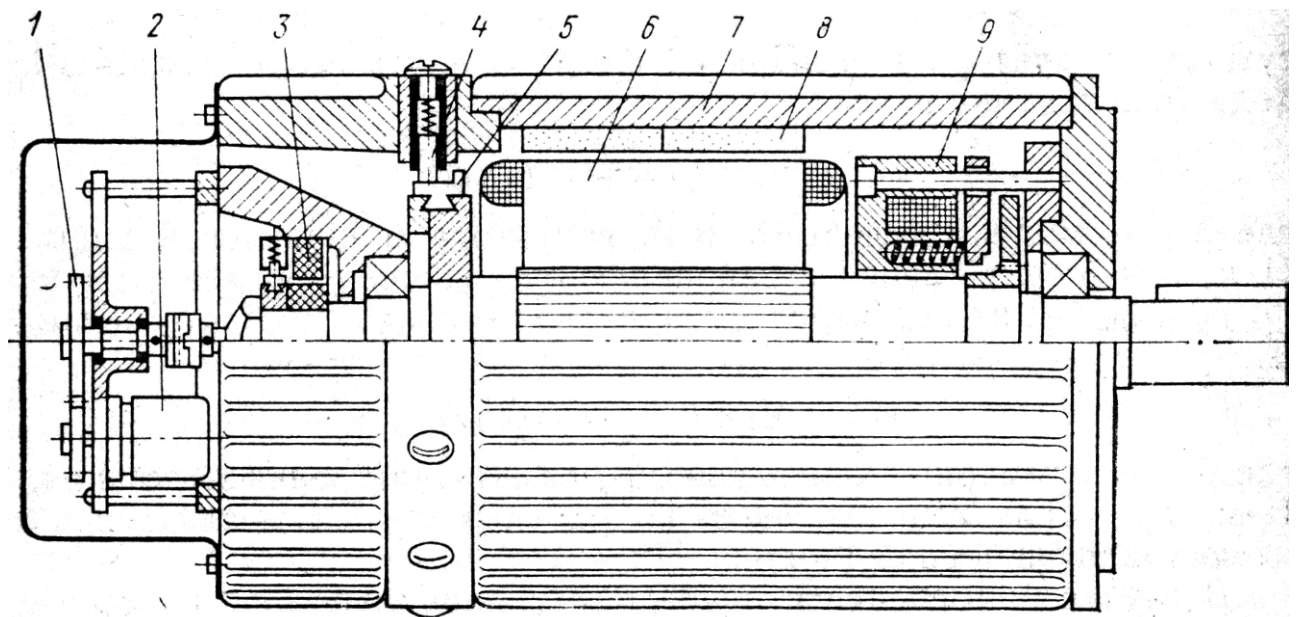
Высокомоментный двигатель: 1 — повышающая передача (мультипликатор) резольвера, 2 — резольвер, 3 — тахогенератор постоянного тока, 4, 5 — коллекторы, 6 — ротор, 7 — корпус статора, 8 — ферритовые полюсы, 9 — электромагнитный тормоз
